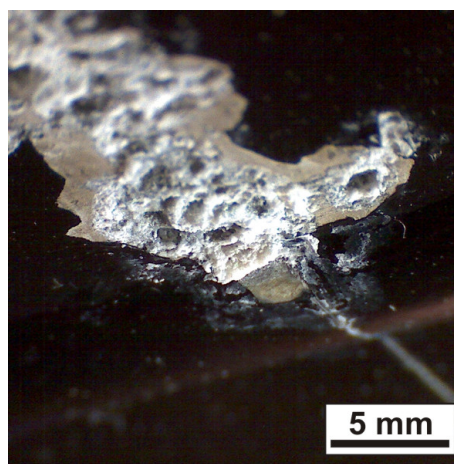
Beschichtetes Versuchsblech der geschweißten Verbindung AZ31 / AA6016 / AlSi12, KTL V2 Oxsilan® 9802, Detailaufnahme aus Bild 86, magnesiumseitige Delaminierung am Ritz
